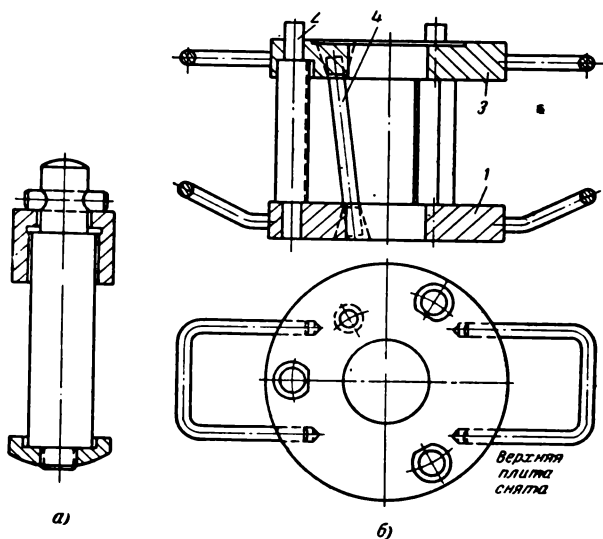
Оправка и сборник для ротора со скошенными пазами.
